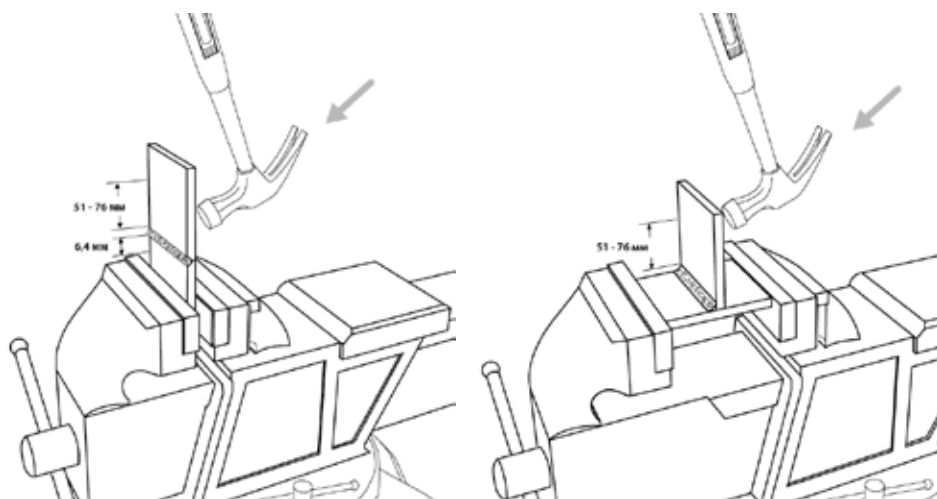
Проверка на прочность сварного соединения.
